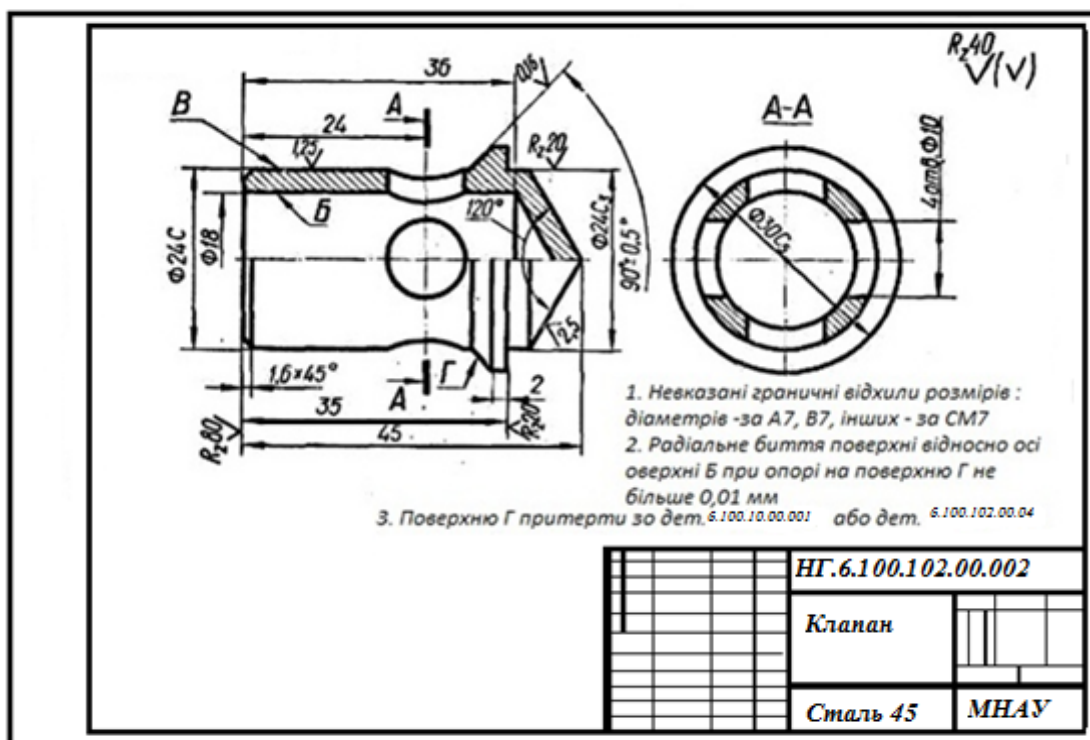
Робоче креслення деталі подвійного зворотного клапана
